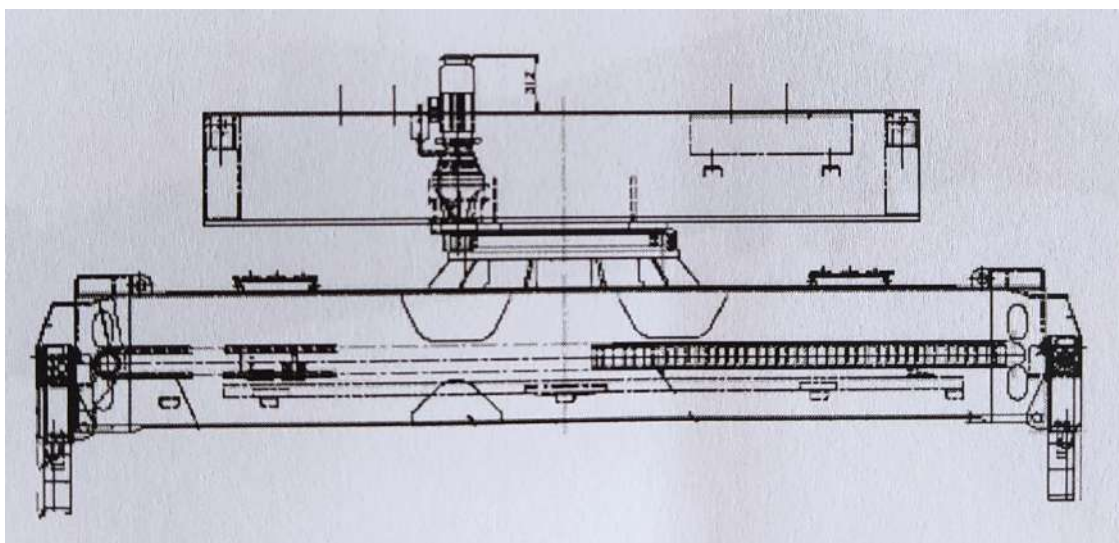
Спредер автоматичний поворотний фіксованої довжини
